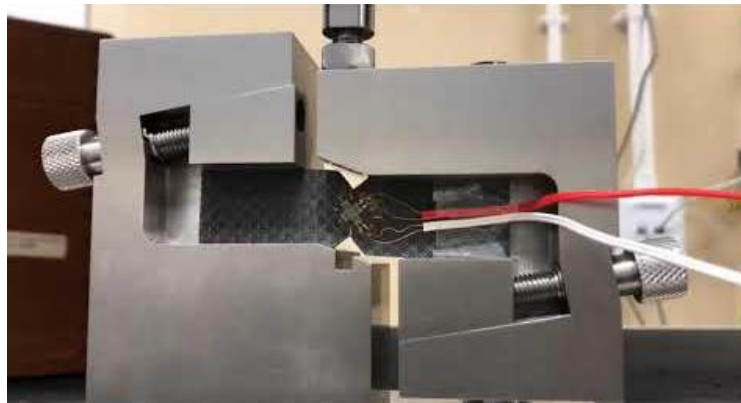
Referencia de diseño para utillaje de ensayo de Iosipescu (SHIMADZU)
